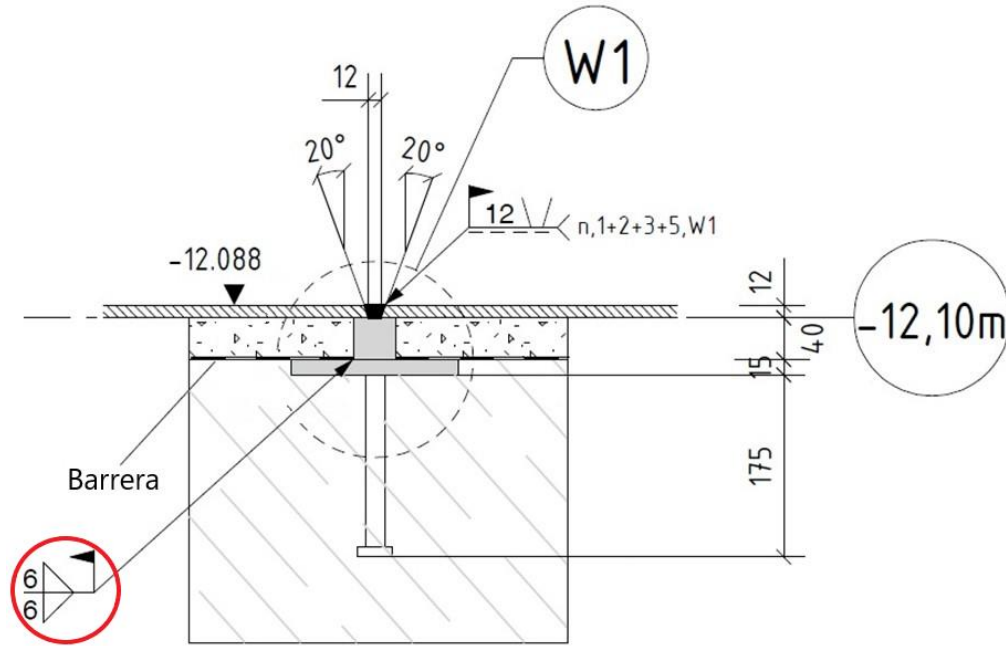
Welding Map que muestra el espesor requerido del cordón de soldadura resaltado con un círculo rojo. Fuente: Imagen extraída de los Welding Map elaborados por CONUAR.
